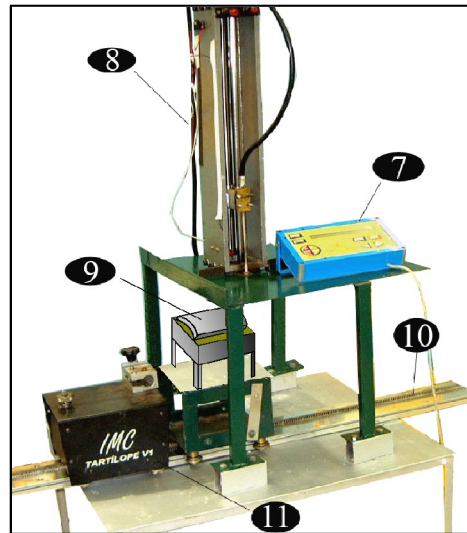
Detalhe do sistema de soldagem automática alojado dentro do Bunker.
